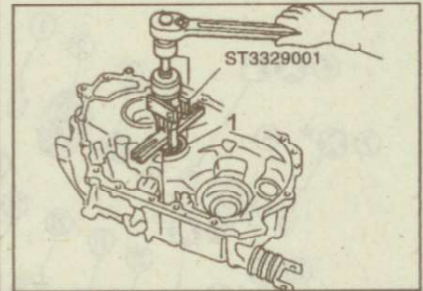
Снятие переднего подшипника (1) вторичного вала с картера коробки передач
